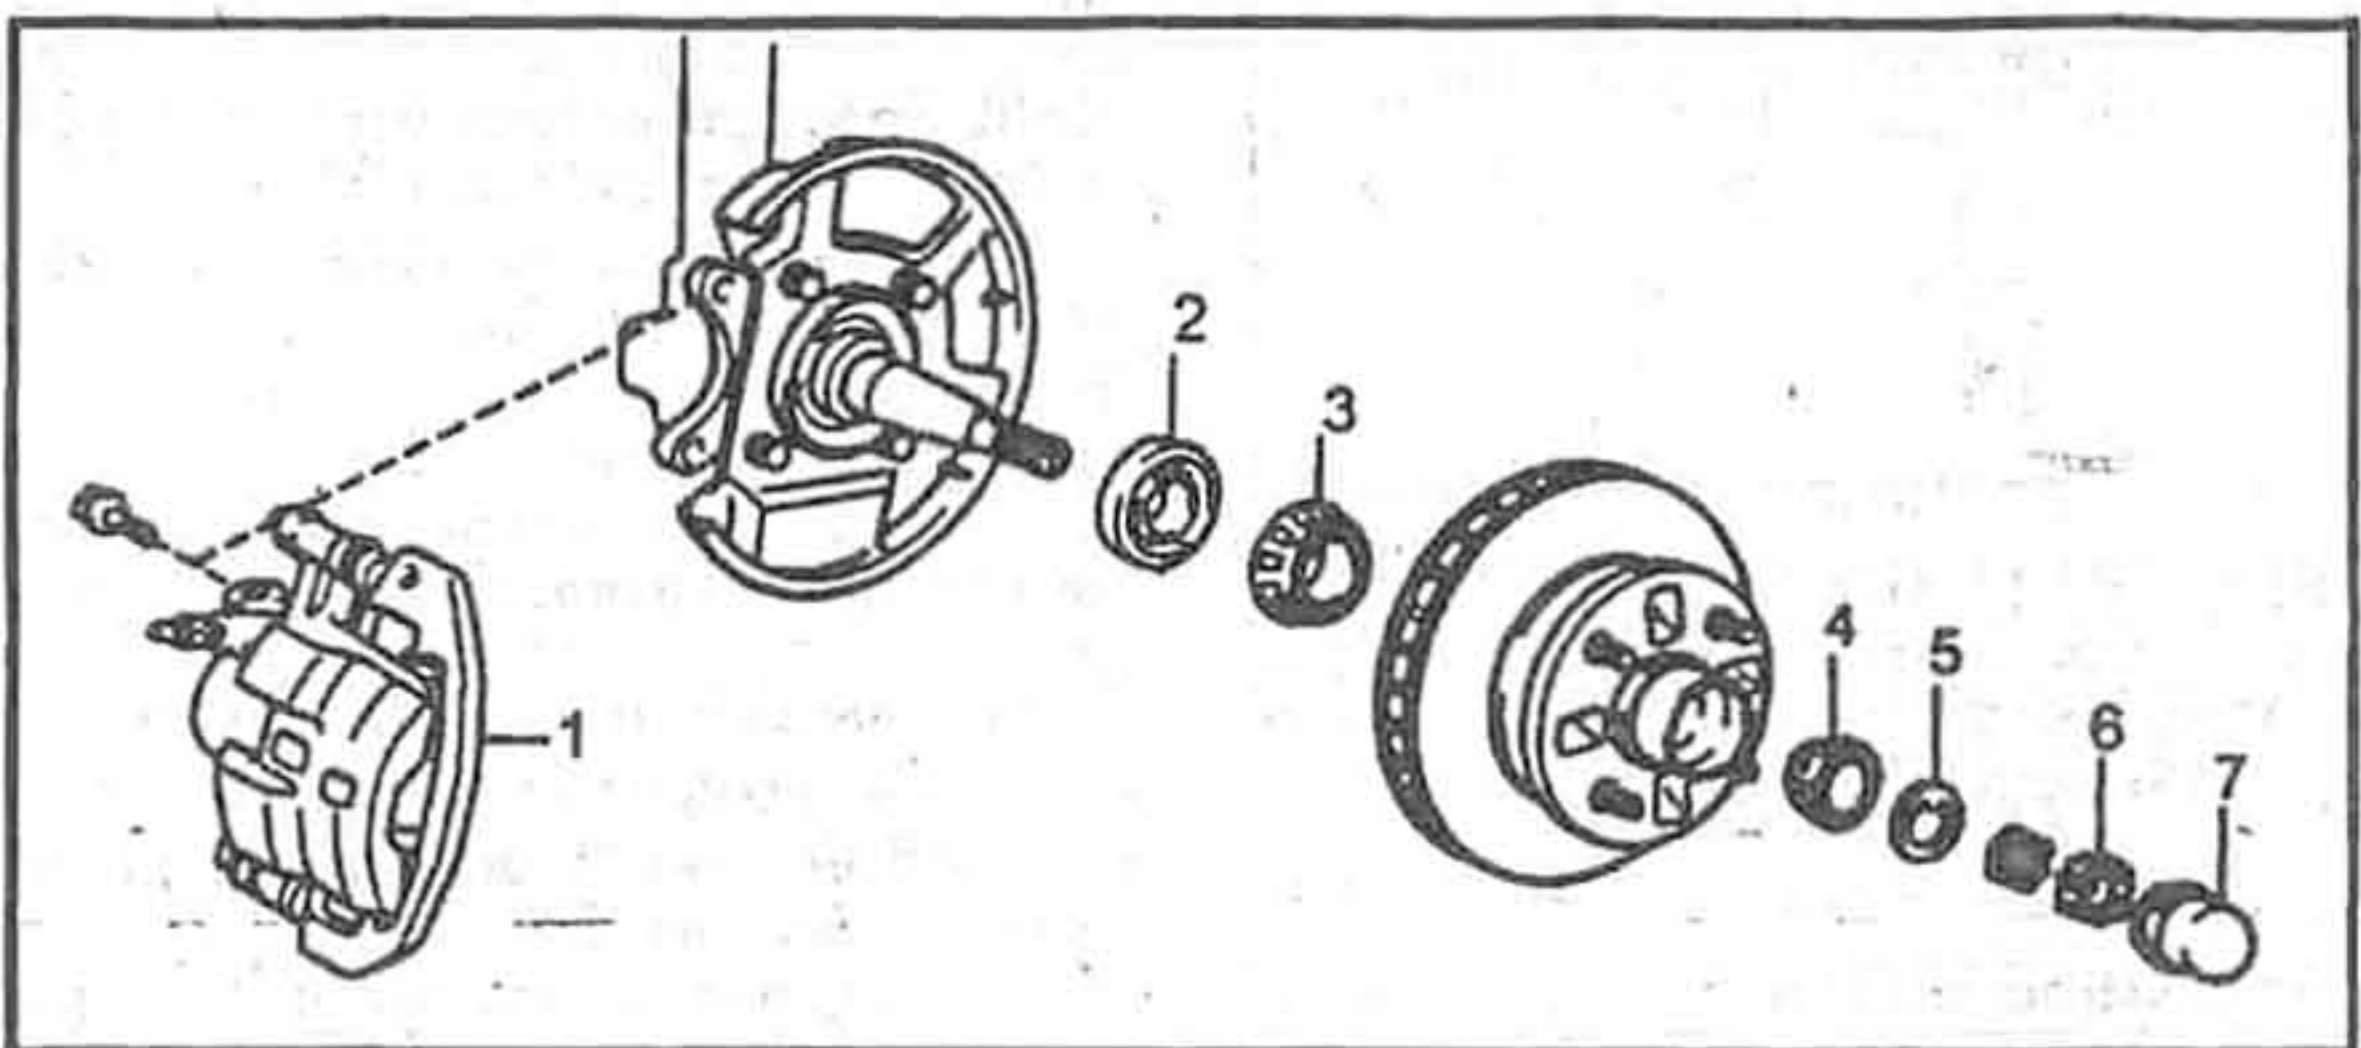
1. Суппорт тормоза. 2. Сальник. 3. Внутренний подшипник. 4. Наружный подшипник. 5. Упорная шайба. 6. Стопорная гайка. 7. Крышка.
